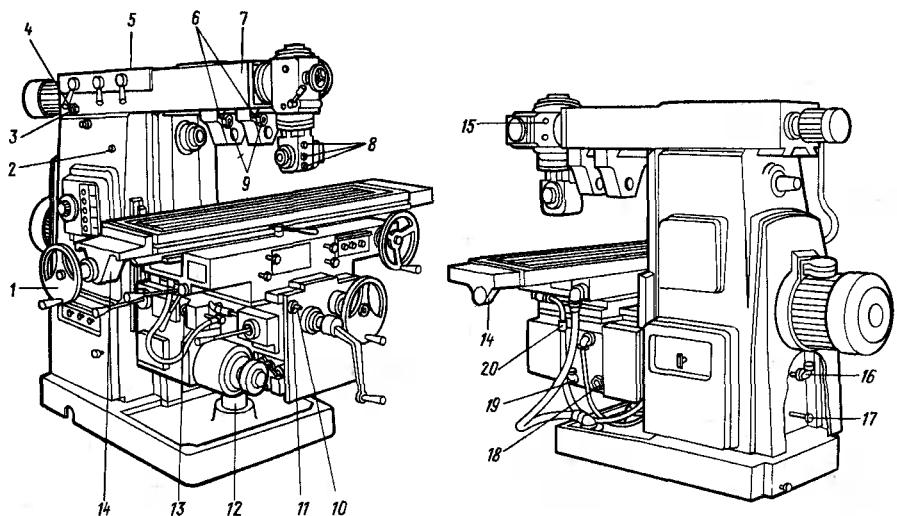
Схема смазки станков 6P82Ш и 6P83Ш
